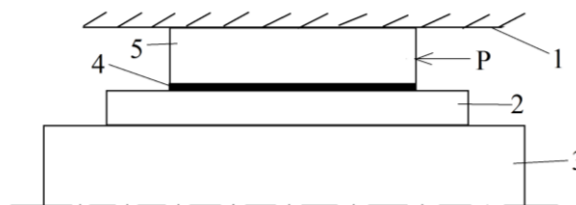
Схема трения сальникового уплотнения. 1 – корпус, 2 – втулка, 3 – вал, 4 – смазочный материал, 5 – сальниковая набивка
